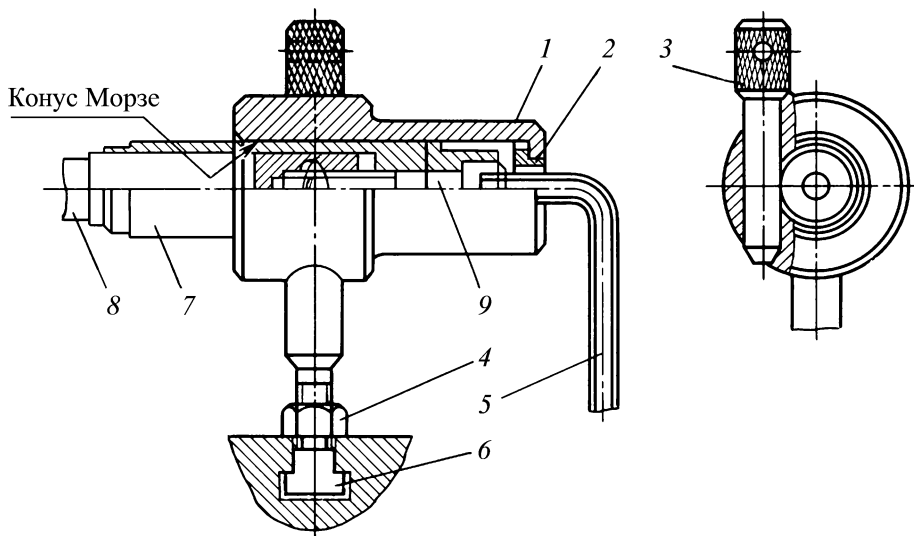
Приспособление для безударного закрепления и извлечения инструмента:
